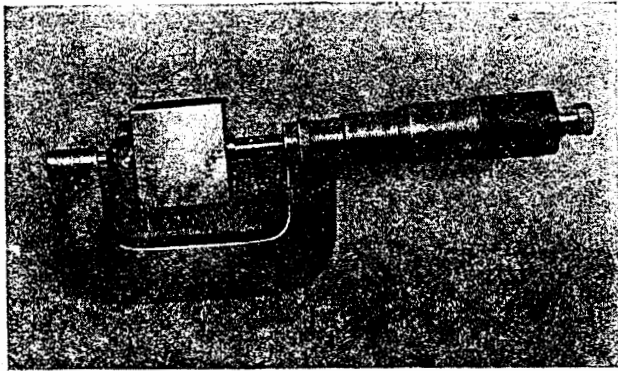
Rollenstößel mit Meßwerkzeug (Werkzeug Nr. 244) vermessen
